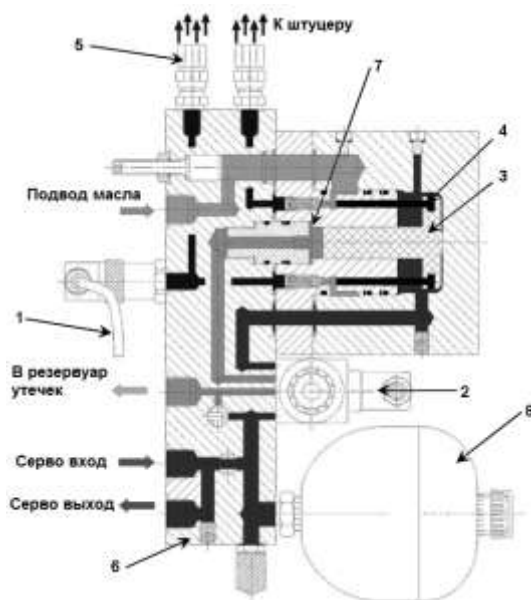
Схема смазочного модуля "Pulse": 1 – электронный контроллер; 2 – электромагнитный клапан; 3 – центральный поршень; 4 – отмеряющий поршень; 5 – запорный клапан; 6 – опорная плита; 7 – регулировочный винт; 8 – аккумулятор
